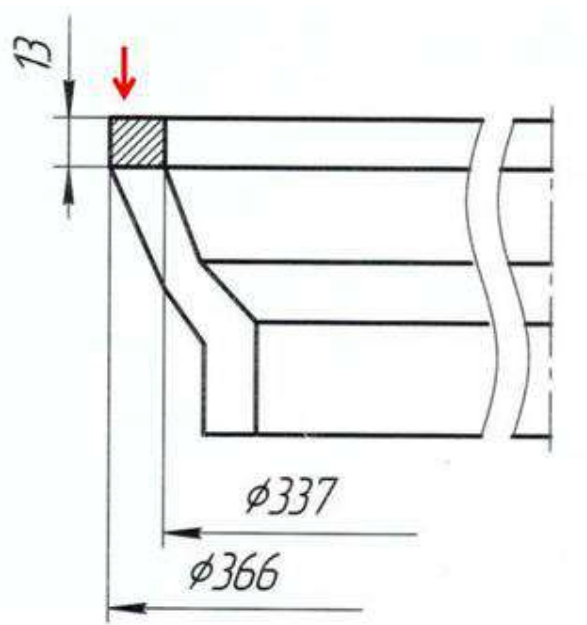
Схема наплавлення 7-ї ділянки
